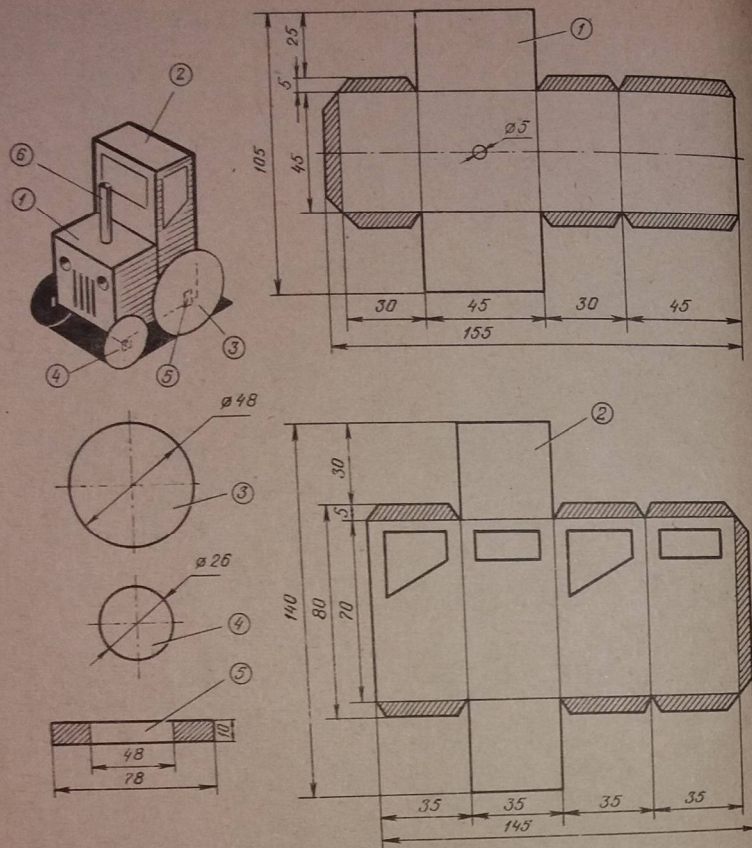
Модель трактора: 1 — капот; 2 — кабина; 3 — заднее колесо; 4 — переднее колесо; 5 — подшипник; 6 — выхлопная труба
